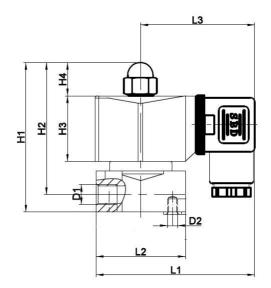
Размеры клапанов Ду6-8 корпус нержавеющая сталь 304
